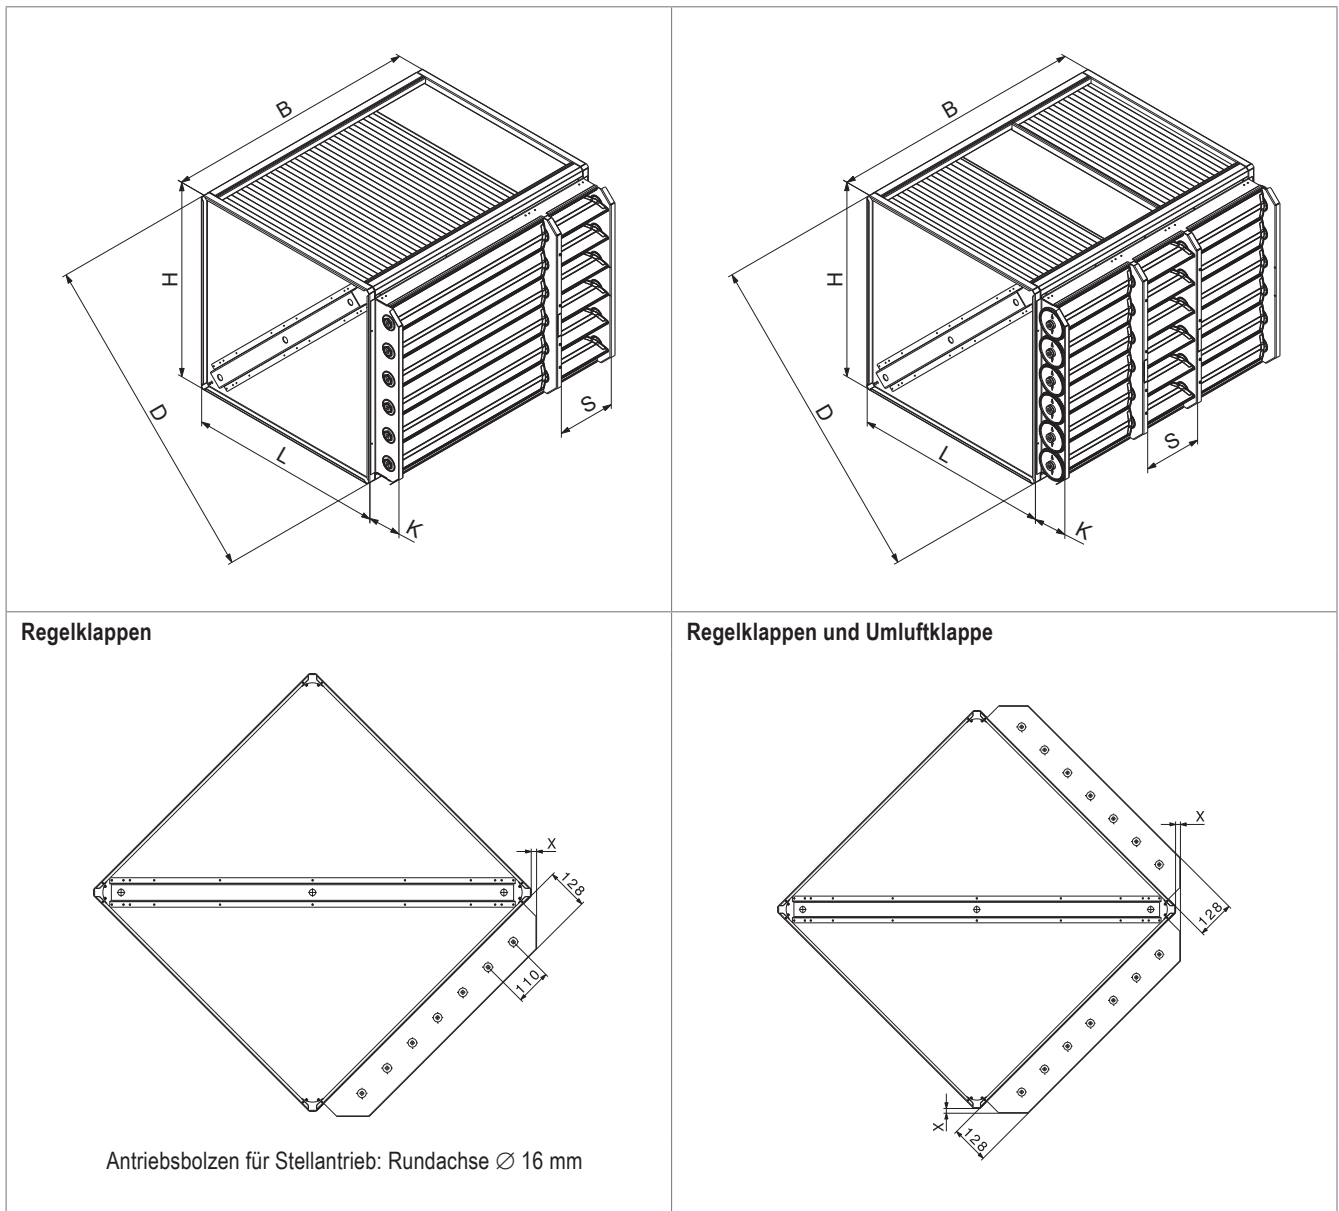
Maßblatt für Plattenwärmetauscher der Ausführung F mit Klappen (Maße in mm)
